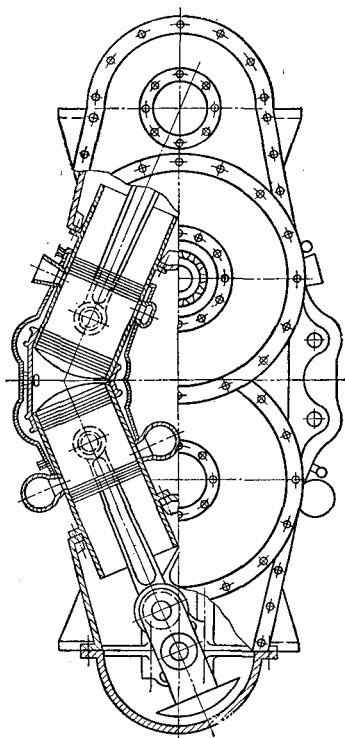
Схема двигателя с цилиндрами, расположенными под углом
